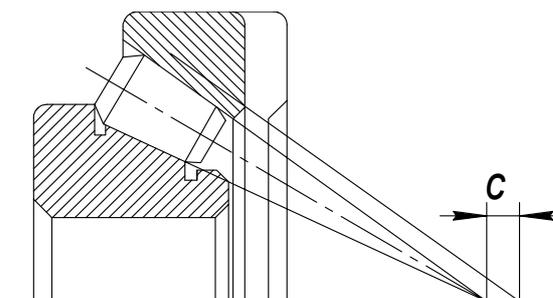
Схема регулирования радиального зазора конического роликоподшипника
